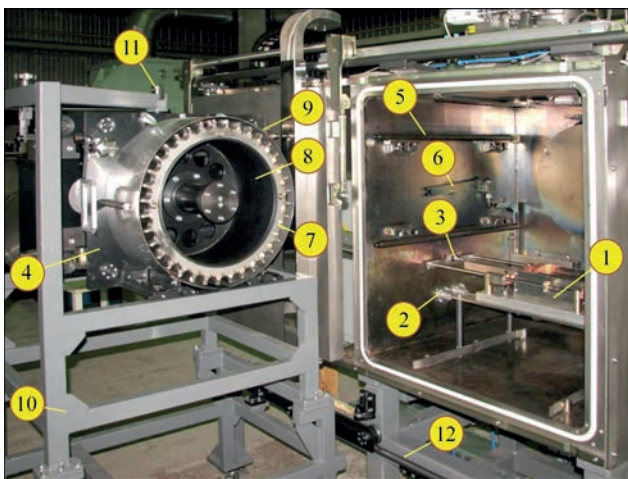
Загальний вигляд більшості механізмів, що пов'язані з ЕПО: 1 – механізм обертання деталей; 2 – привід цього механізму; 3 – механізм повздовжньої подачі деталей; 4 – барабанний магазин деталей; 5 – рейки підвіски магазину в камері; 6 – привід магазину; 7 – змінний вкладиш з комірками для деталей; 8 – поворотний барабан магазину; 9 – зовнішня обичайка магазину; 10 – рама завантажувального пристрою; 11 – поворотний вузол підвіски для двох барабанних магазинів цього пристрою; 12 – горизонтальна опорна рейка цього пристрою
